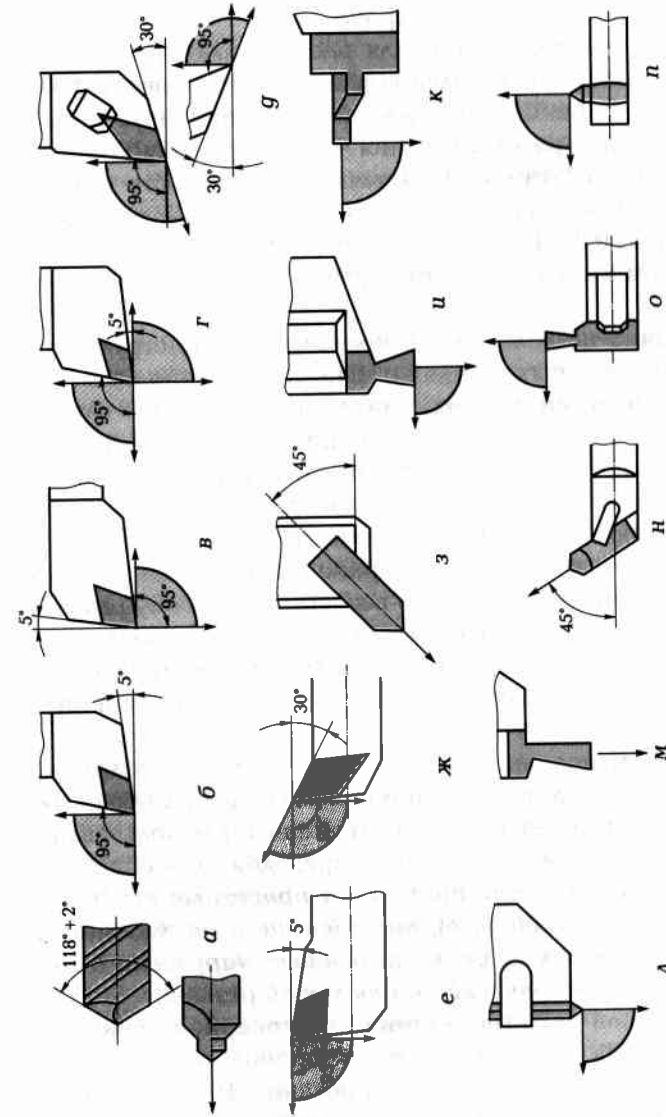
Номенклатура режущего инструмента для токарных станков с ЧПУ с указанием зон направления рабочей подачи:
